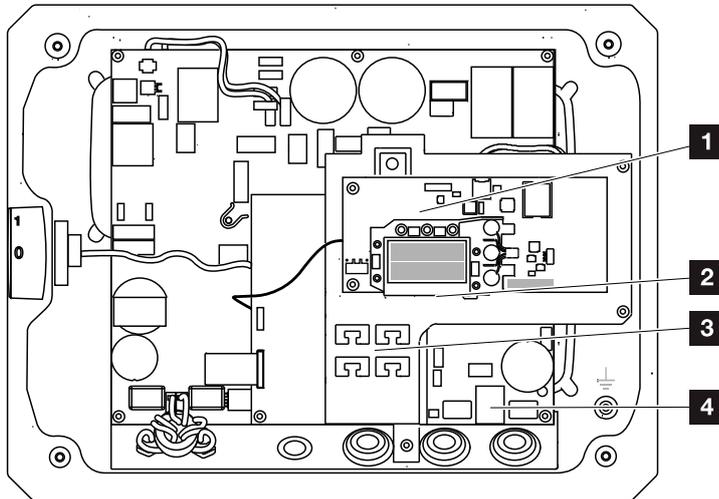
PIKO-Wechselrichter 3.0 (Innenansicht)
